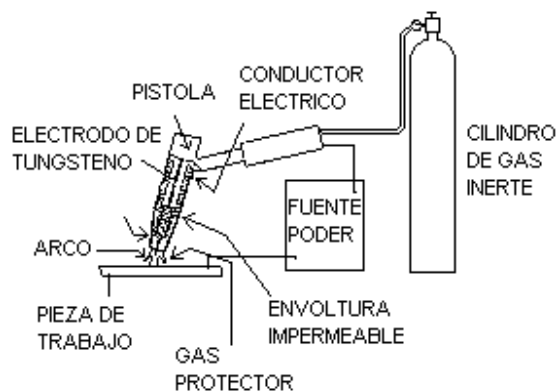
Equipo proceso de soldadura TIG.
